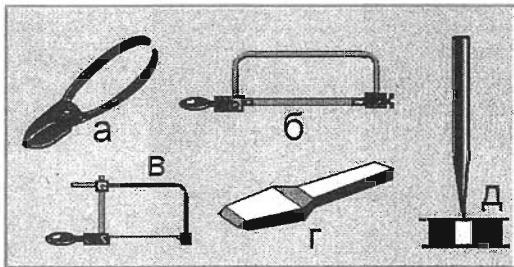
Режущий инструмент: а – ножницы по металлу; б – слесарная ножовка; в – слесарный лобзик; г – зубило; д – пробойник
